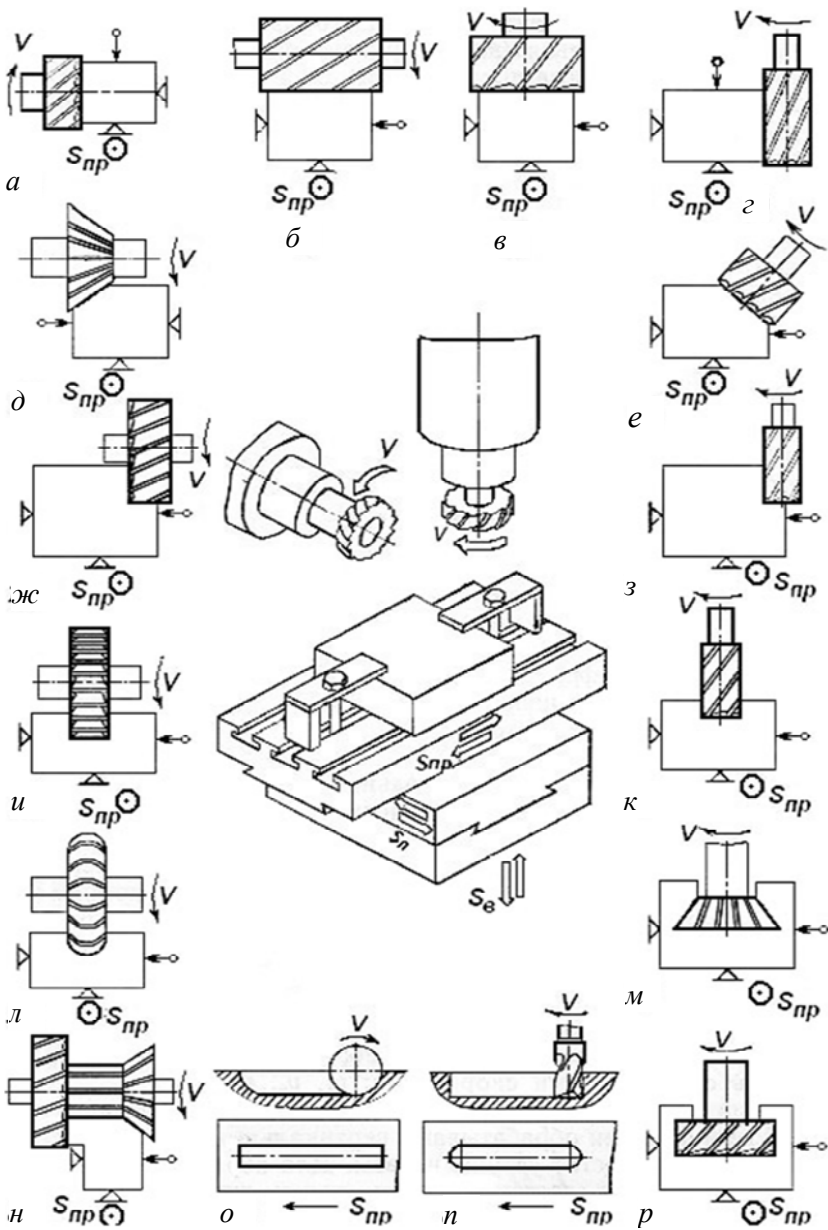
Схемы обработки поверхностей фрезерованием
